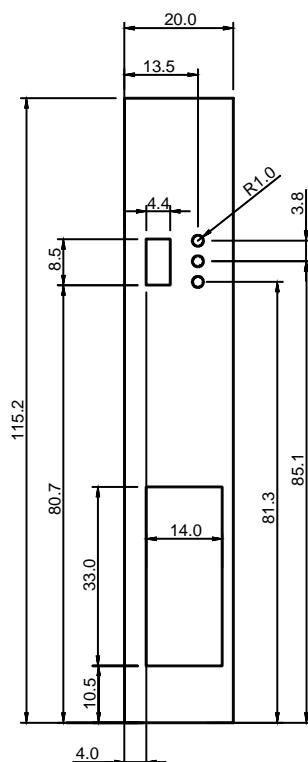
Abmessungen Frontblende für CIFX 80-RE
